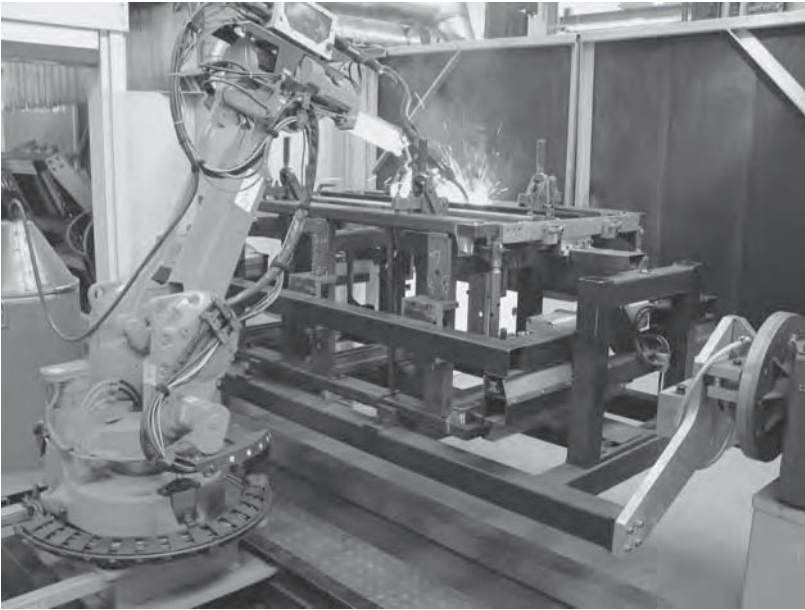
Célula robotizada de soldadura al arco. (Cortesía ABB).
